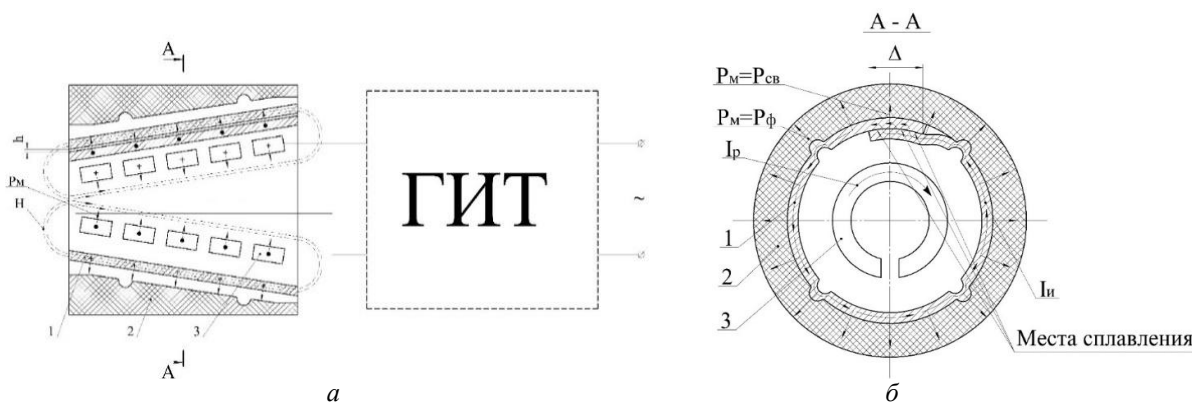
Схема МИС штампосварной детали: а, б – начало и окончание процесса
